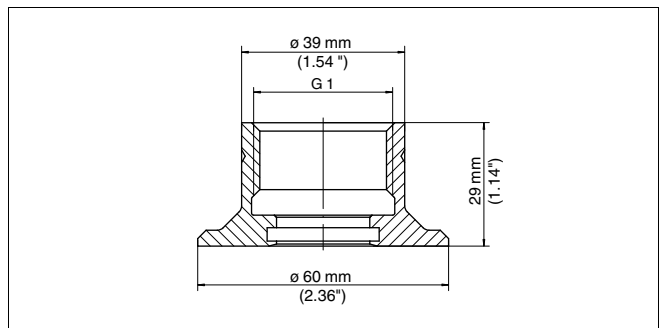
Medidas racor soldado G1 A según DIN 3852-X
